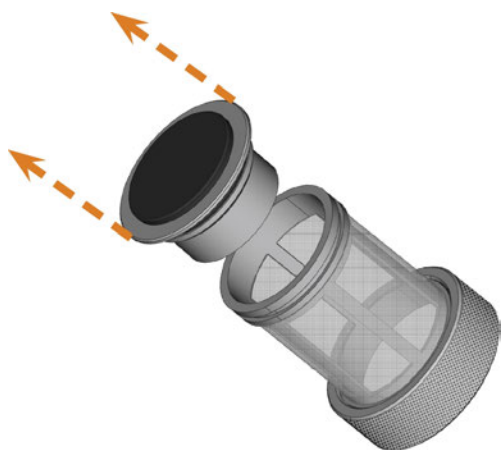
RETIRAR EL FILTRO DE CARBÓN
